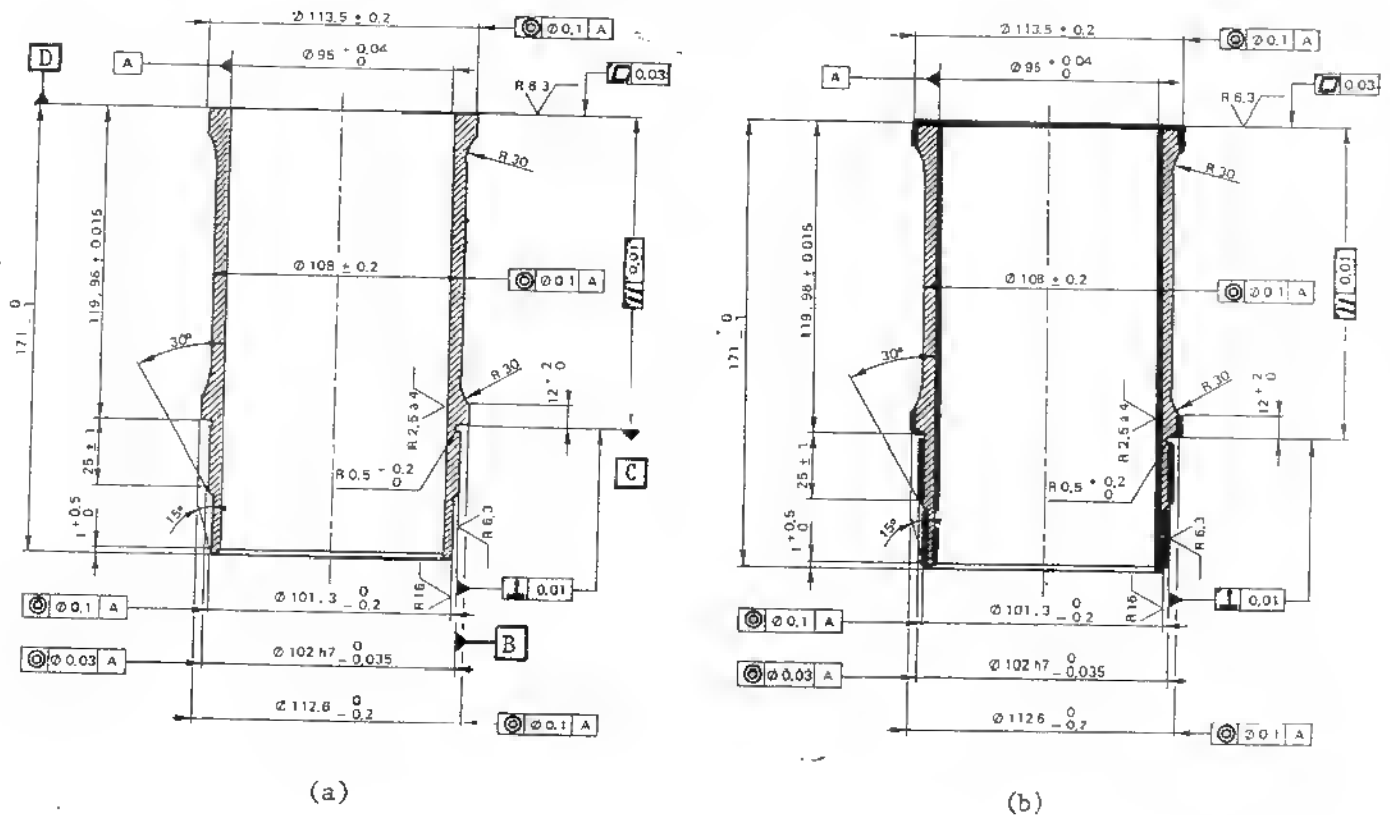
(a) Dessin de fabrication d'une chemise de moteur à explosion.
